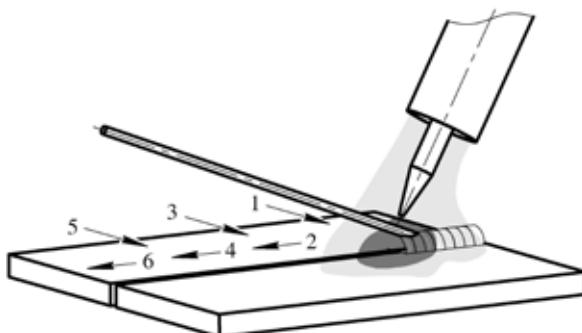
Пример манипуляции присадочной проволокой при TIG сварке.
